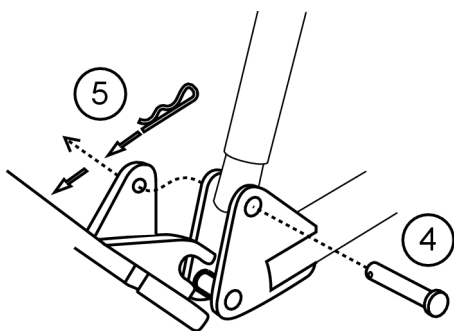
Установка переходника для шлифовки кромок, операции 4—5.
